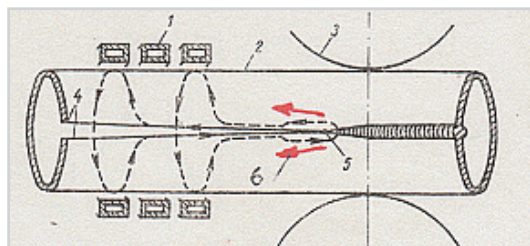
Схема индукционного метода высокочастотной сварки труб
